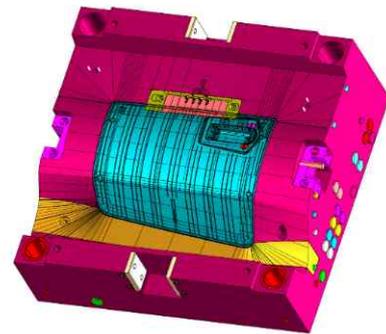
CAD Modell eines Werkzeugeinsatzes zur Fertigung einer Handschuhfachabdeckung
